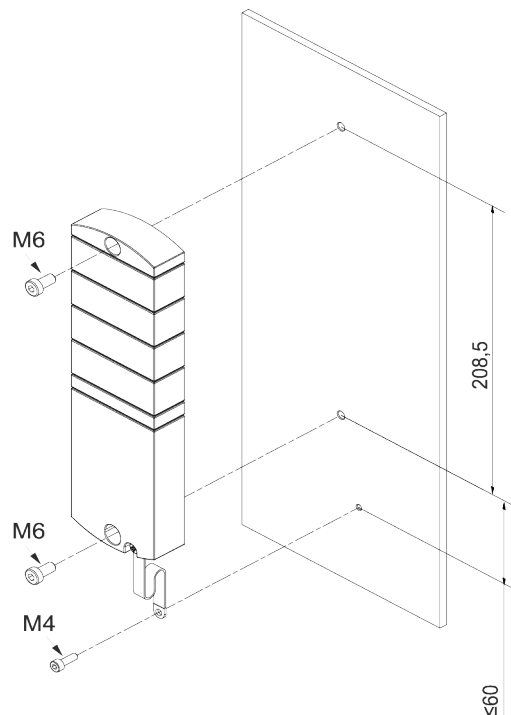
Gerät befestigen. Abmessungen in mm (Abbildung ähnlich)
